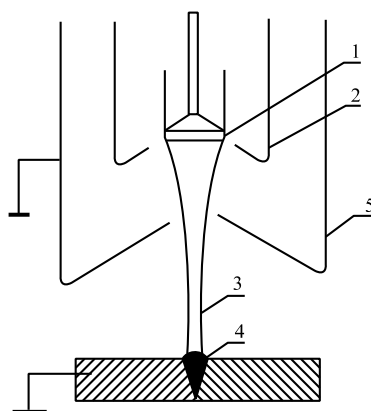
Схема сварочной пушки для ЭЛО:
